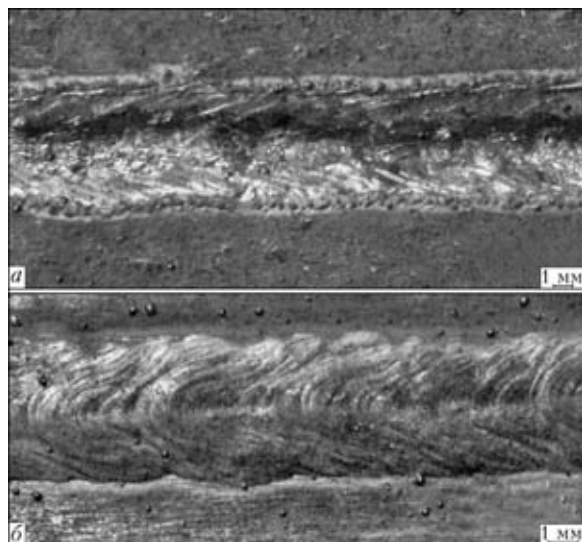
Вид поверхности стыкового соединения легированной стали после лазерной сварки без (а) и с расплавлением (б) присадочной проволоки
